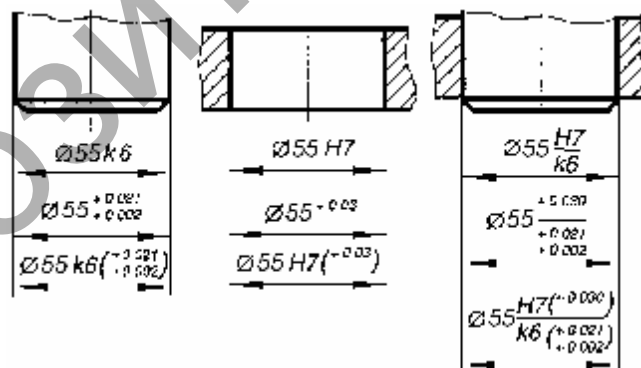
Примеры обозначения полей допусков и посадок на чертежах
